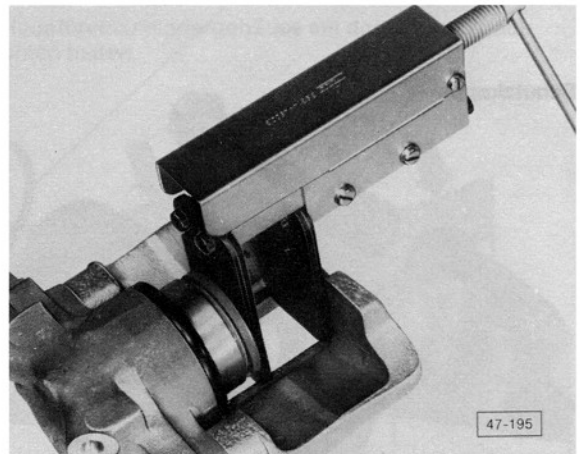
Kolben mit Kolbenrücksetzvorrichtung in den Zylinder drücken
